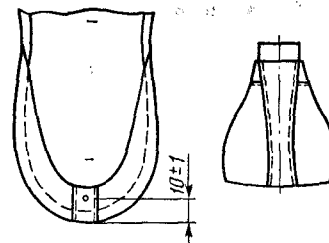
Схема надевания заготовки верха на колодку и установки пяточной части
